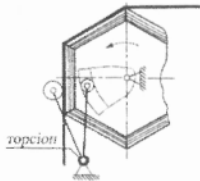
Схема модернізованого пристрою з пружним компенсатором коромисла
